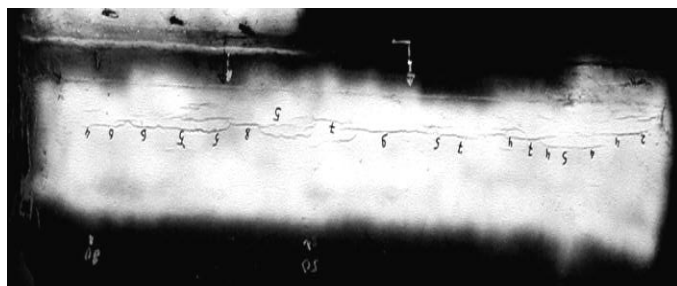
Вид поверхности дефекта катушки №1315: знаком обозначено намеченное место ремонта сваркой
